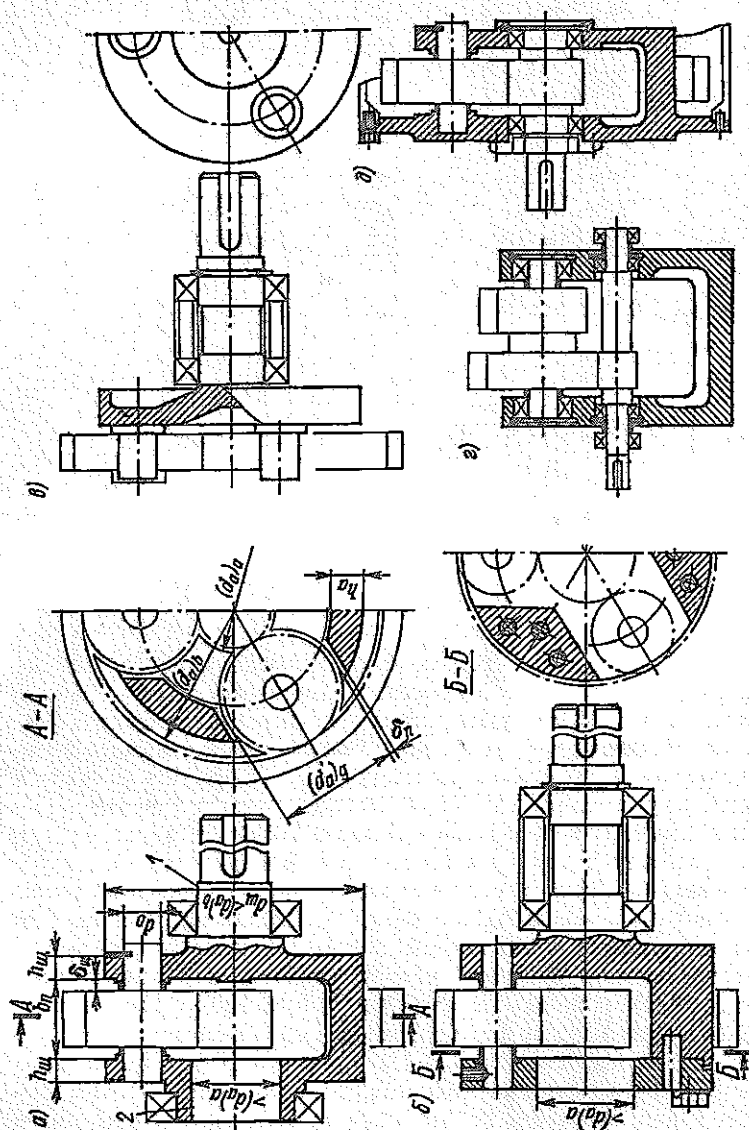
Конструкции неподвижного водила: а — неразъемное с симметричным расположением между опорами; б — разъемное с консольным расположением на опорах; в — с одной щекой и консольными осями сателлитов; г — без подвода внешнего момента (для передачи 3к); д — с вращающейся водило с фланцевым креплением к корпусу
